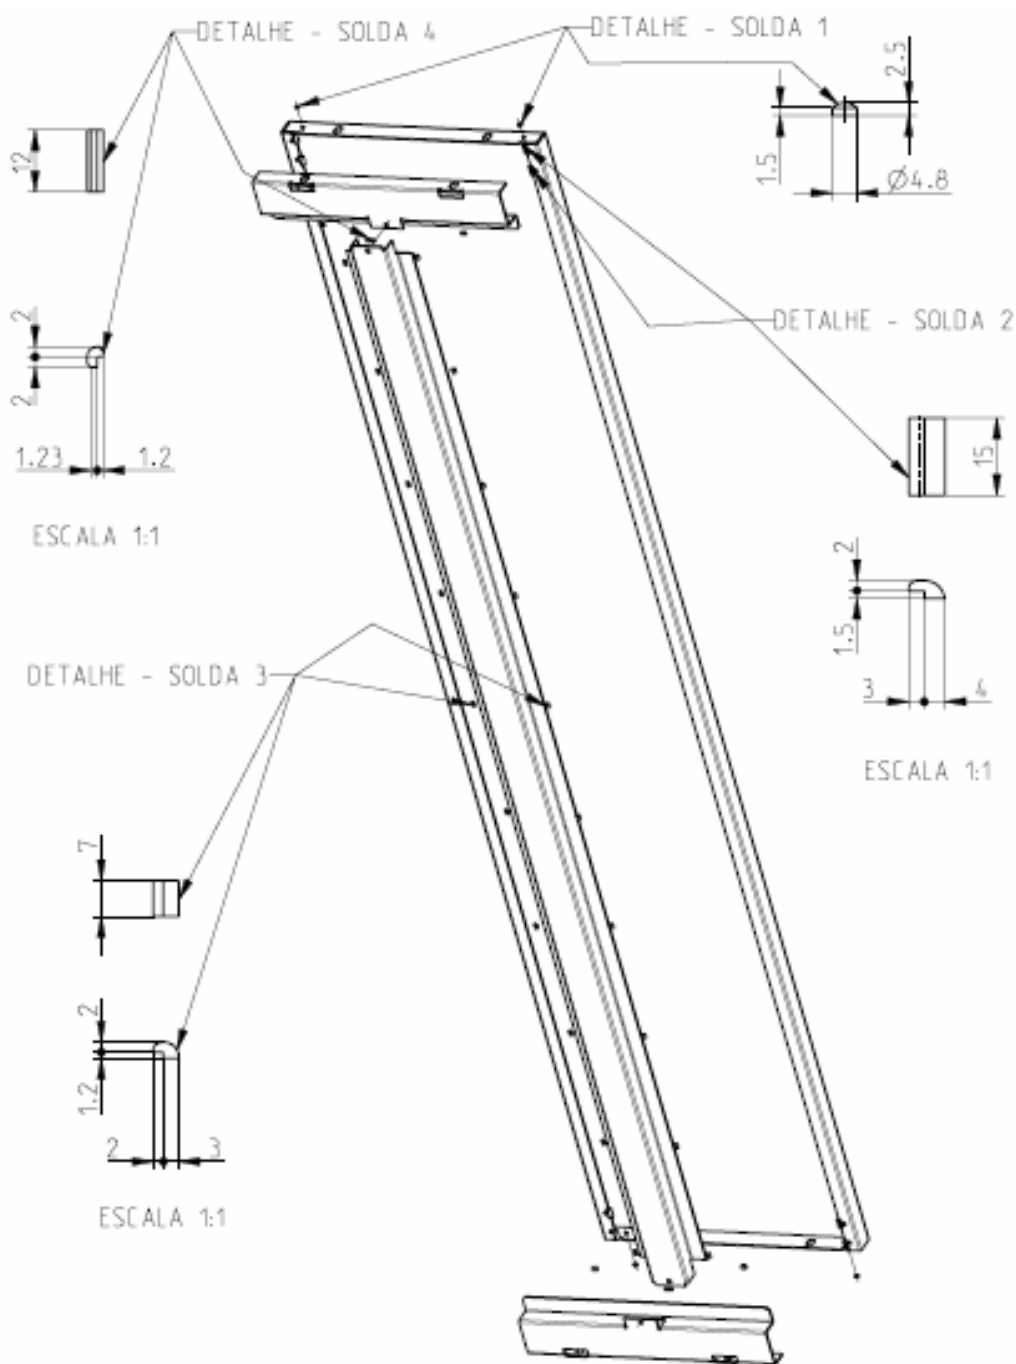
Detalhes dos componentes e dos cordões de solda de um painel soldado
